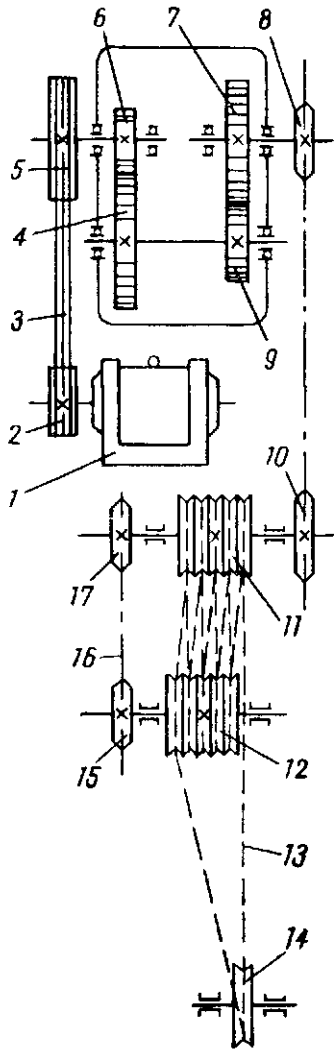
Кинематическая схема привода платформы кормораздатчика РКС-3000:
